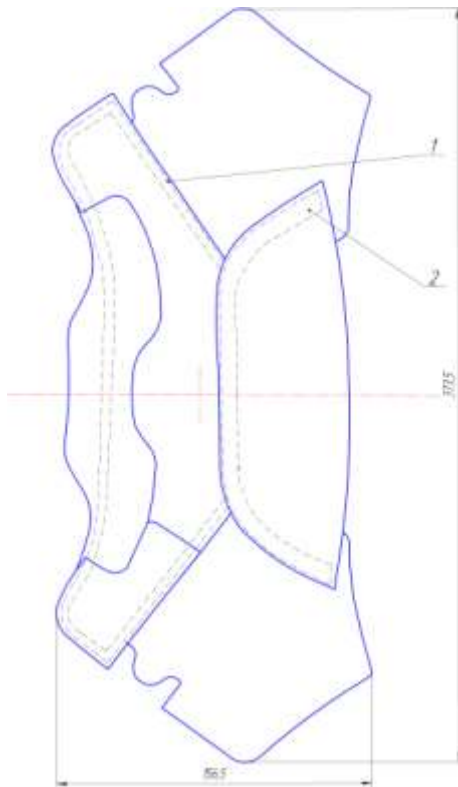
Контуры деталей верха обуви и соединительных строчек
